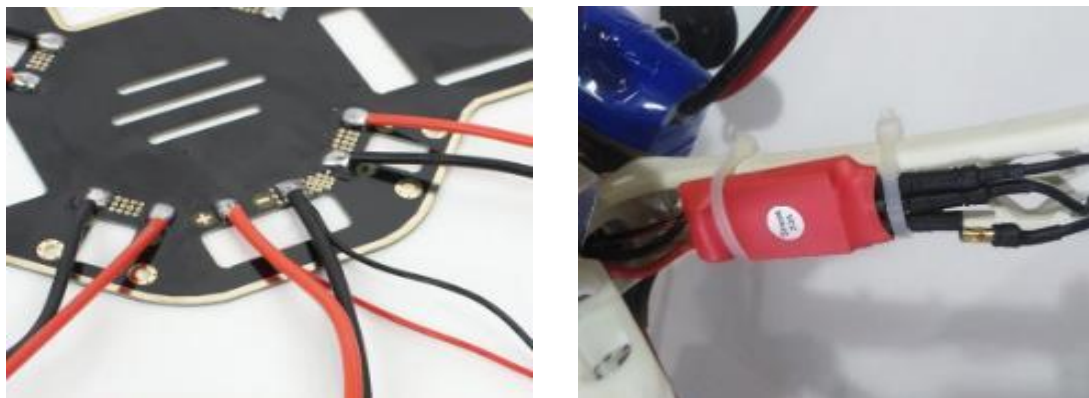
Soldado y sujeción de ESC al chasis
